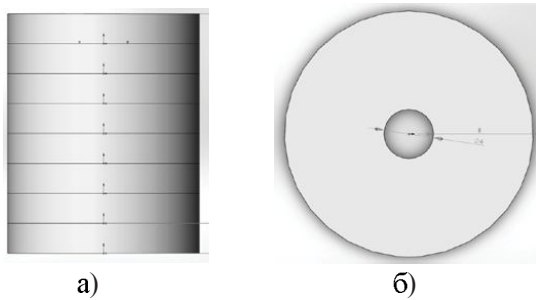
Вид пьезоактюатора сбоку (а) и сверху (б)
